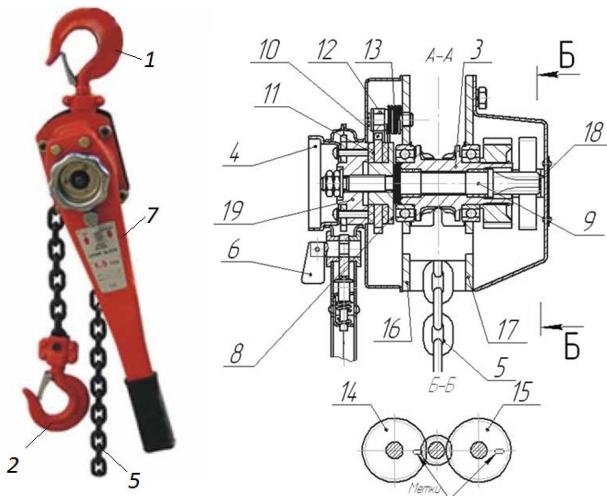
Ручная таль с двухступенчатым редуктором
